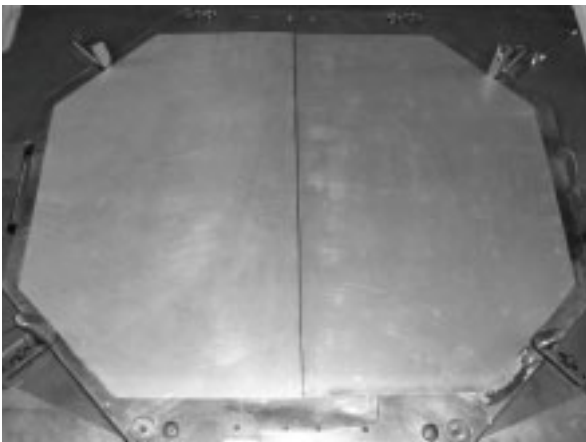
lasergeschweißte tailored blank Platine
